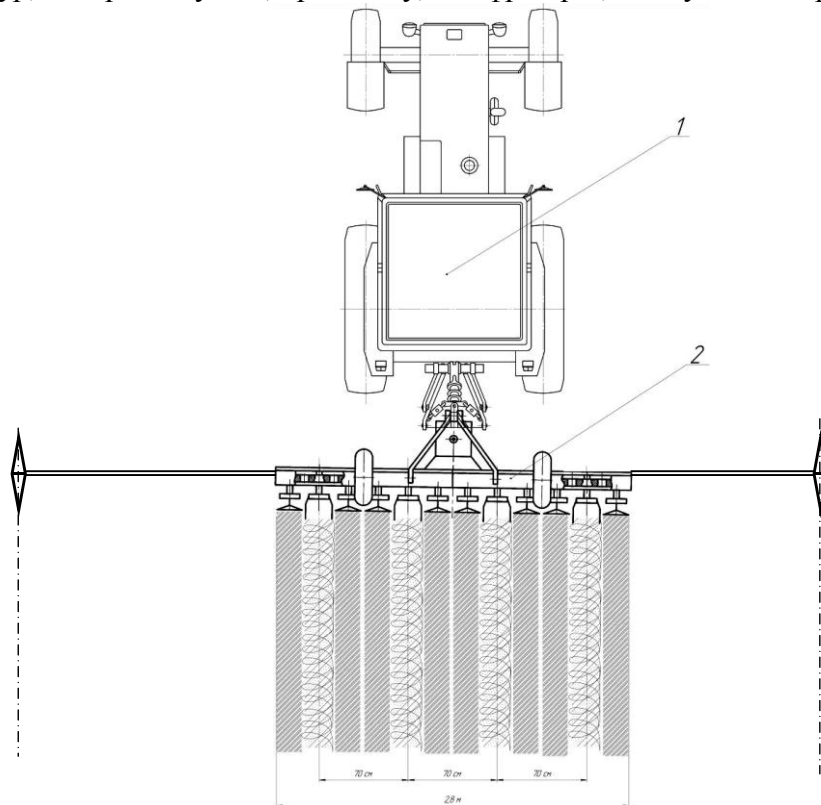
Схема культиваторного агрегату в складі трактора класу 1,4 (поз. 1) і фрезерної машини ФМ-2 (поз. 2)
